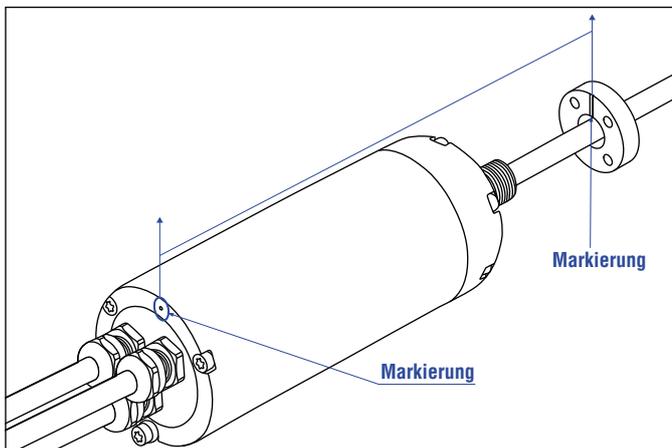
Magnetausrichtung eines Ringmagneten für RM5 EtherNet/IP™ mit interner Linearisierung
